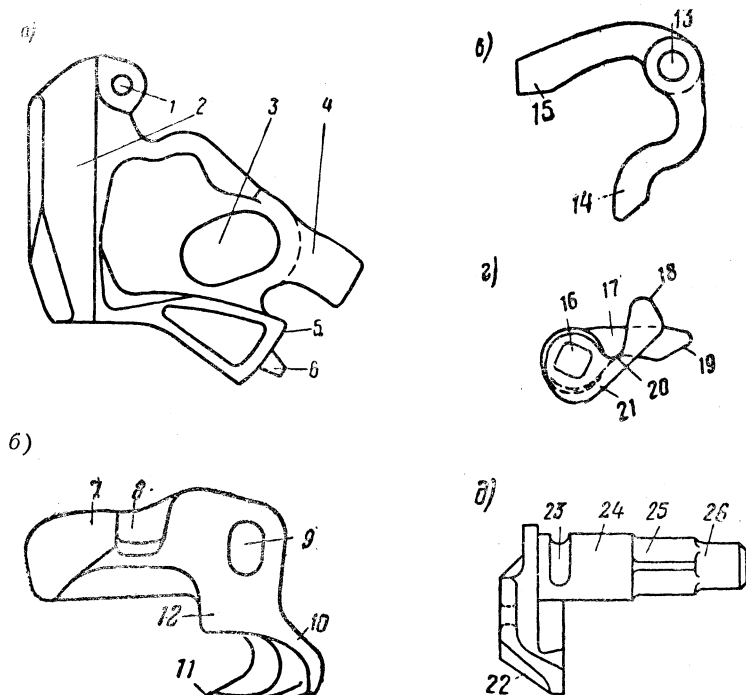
Части автосцепки, расположенные в головке корпуса:
